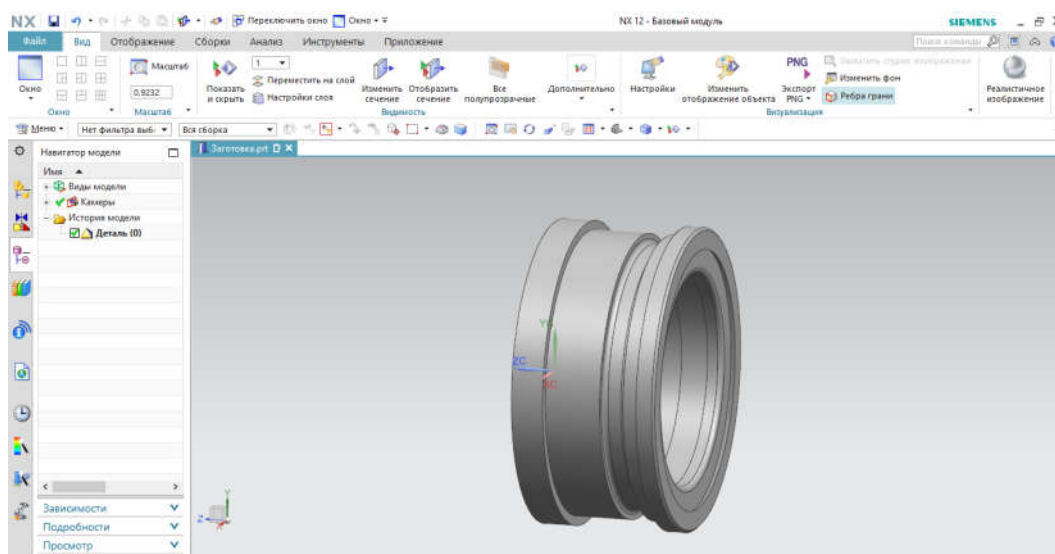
Подготовка 3D модели изделия в NXCAD
